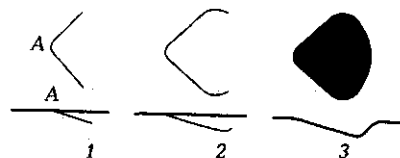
Схема образования поверхностного выкрашивания (питтинга) на рабочей дорожке подшипника качения:
